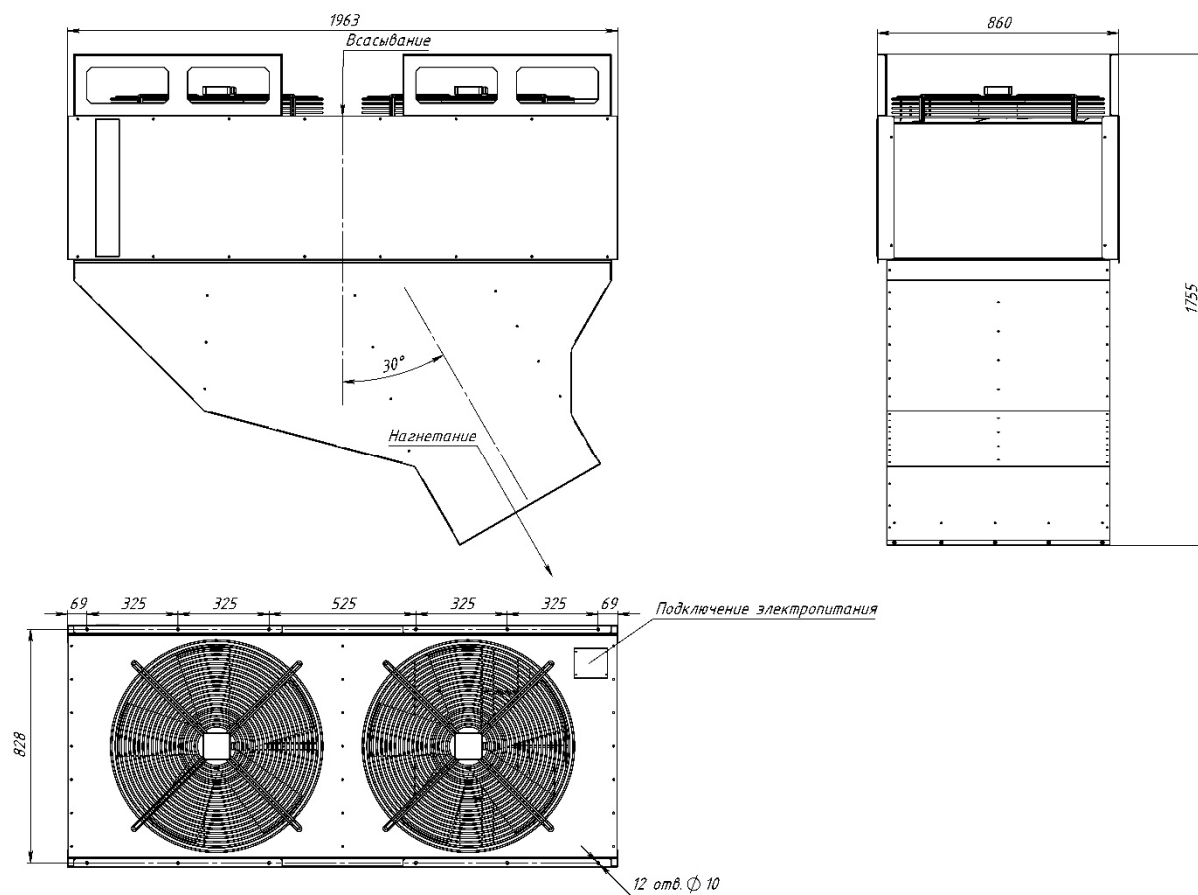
Габаритные и присоединительные размеры SA1 17250 Z
